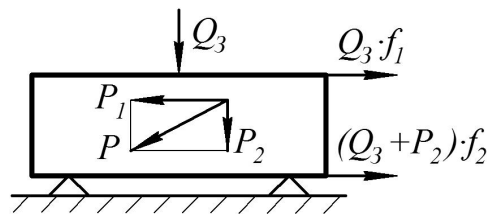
Схема різання для визначення сили закріплення для операцій фрезерування
